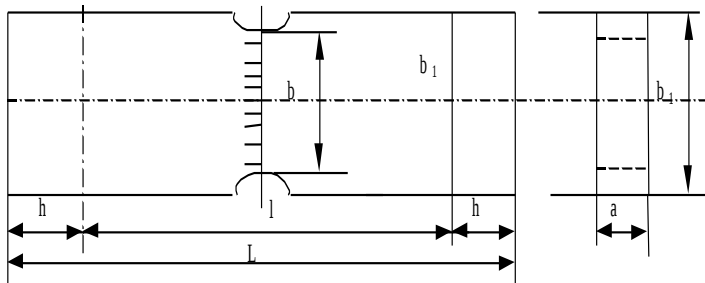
Образец для определения прочности металла сварного шва
